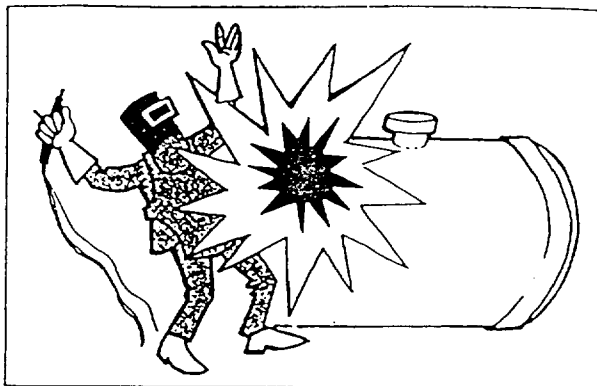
EXPLOSION DUE A UN DEGAZAGE INCOMPLET
